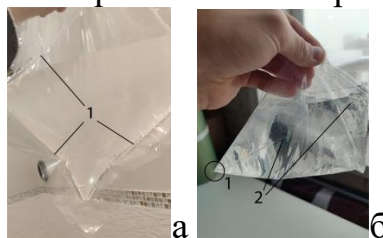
а) Демонстрация проверки соединительного шва 1 на герметичность; б) сварное соединение «нулевой шов»: 1 – угловое соединения пакета, 2 – спаянный шов, выполненный отрезным роликом
